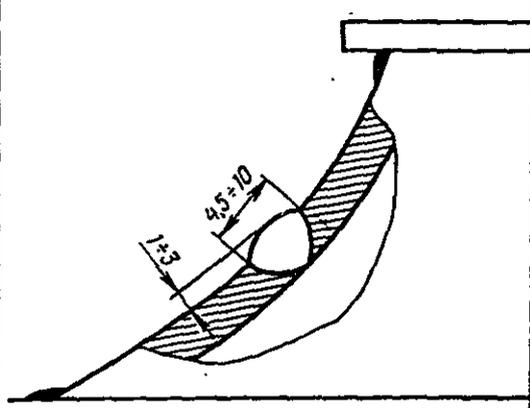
Размеры сварных швов на корпусе камеры сгорания
